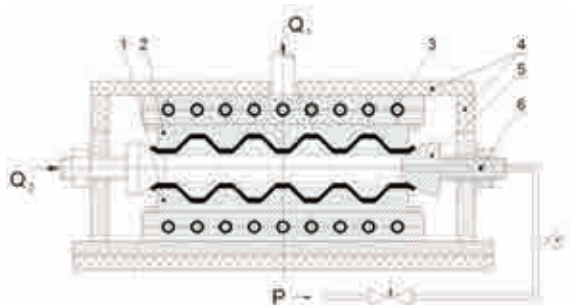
Схема экспериментального БПТФ трубных заготовок:
